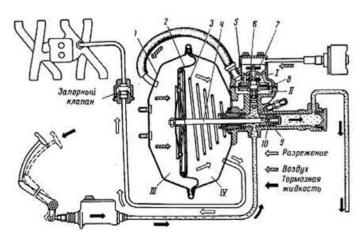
Схема гидровакуумного усилителя автомобиля ГАЗ-53-12 (момент торможения): I, H, III, IV — полости; 7 — корпус; 2 — диафрагма; 3 — пружина; 4 — шток; 5 — пружина; 6 — вакуумный клапан; 7— атмосферный клапан; 8— поршень клапана управления; 9— манжета поршня; 10 — клапан поршня
